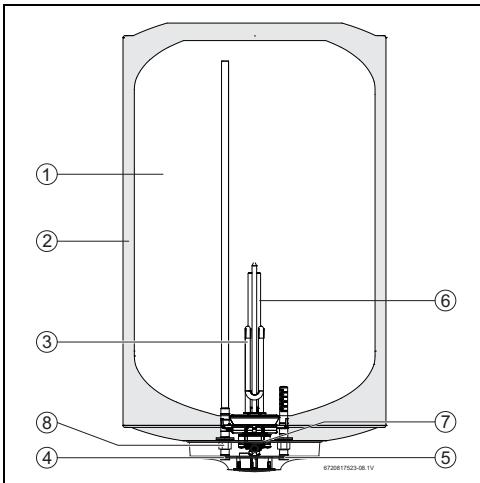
Конструкция бака (здесь: Tronic 2000 T)
